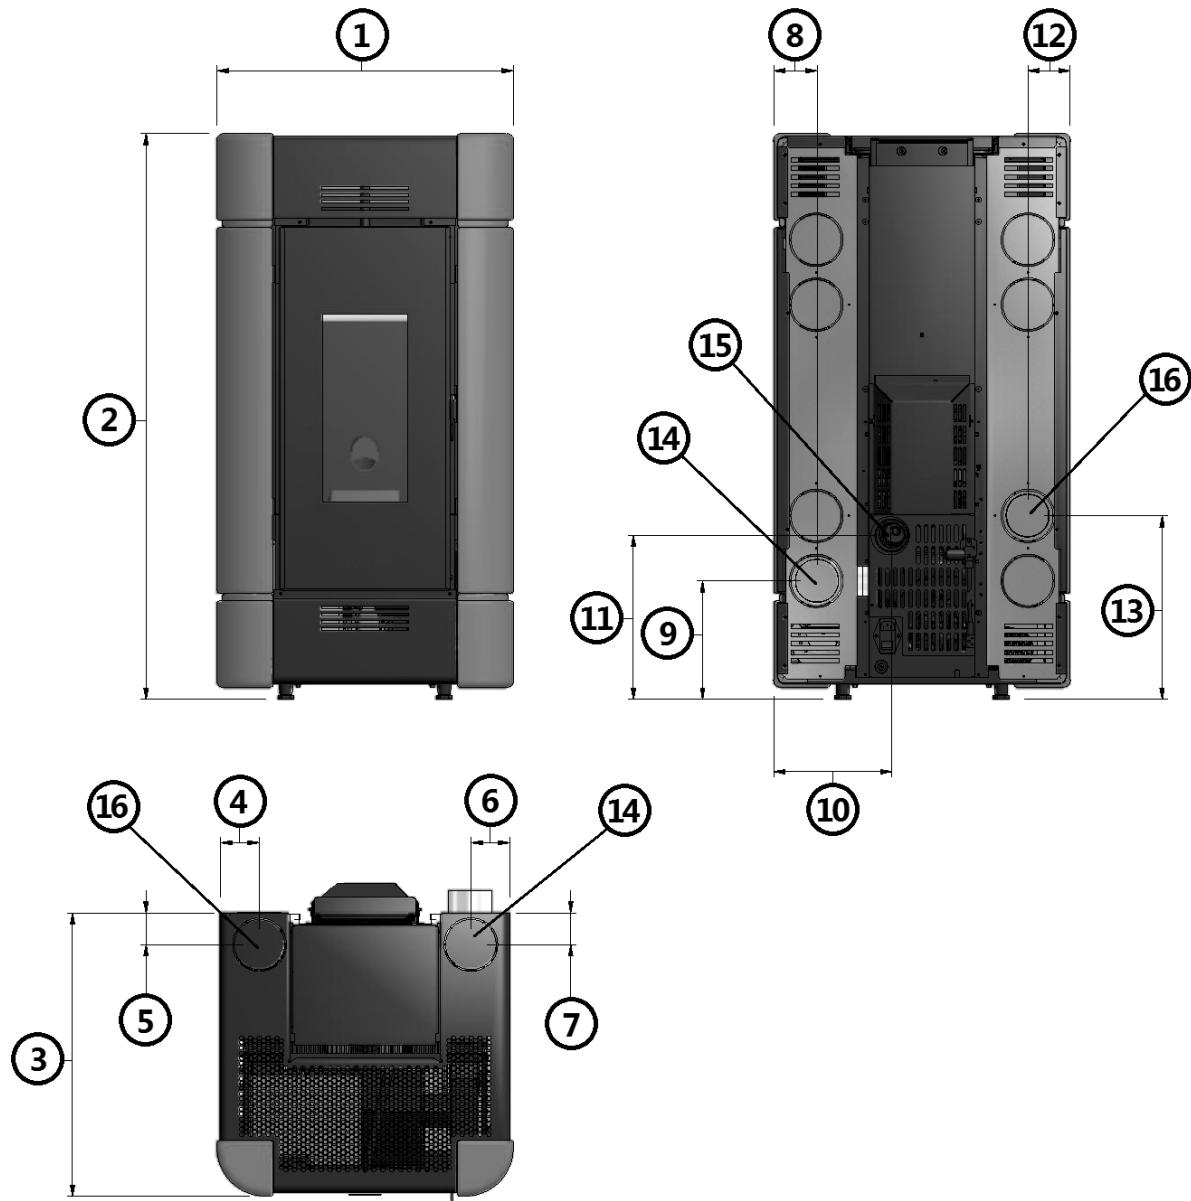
Γενικές διαστάσεις: Sire³ Plus 11KW
